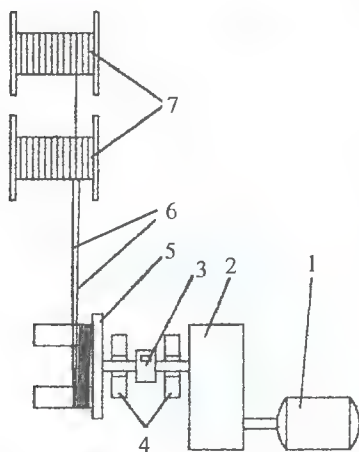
Принципиальная схема намоточного станка: 1 — электродвигатель; 2 — редуктор; 3 — счетчик; 4 — подшипники; 5 — шаблон; 6 — обмоточный провод; 7 — катушки
